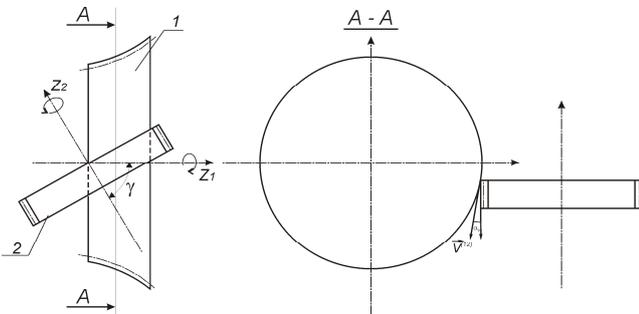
Схема формообразования квазиглобоидной заготовки
